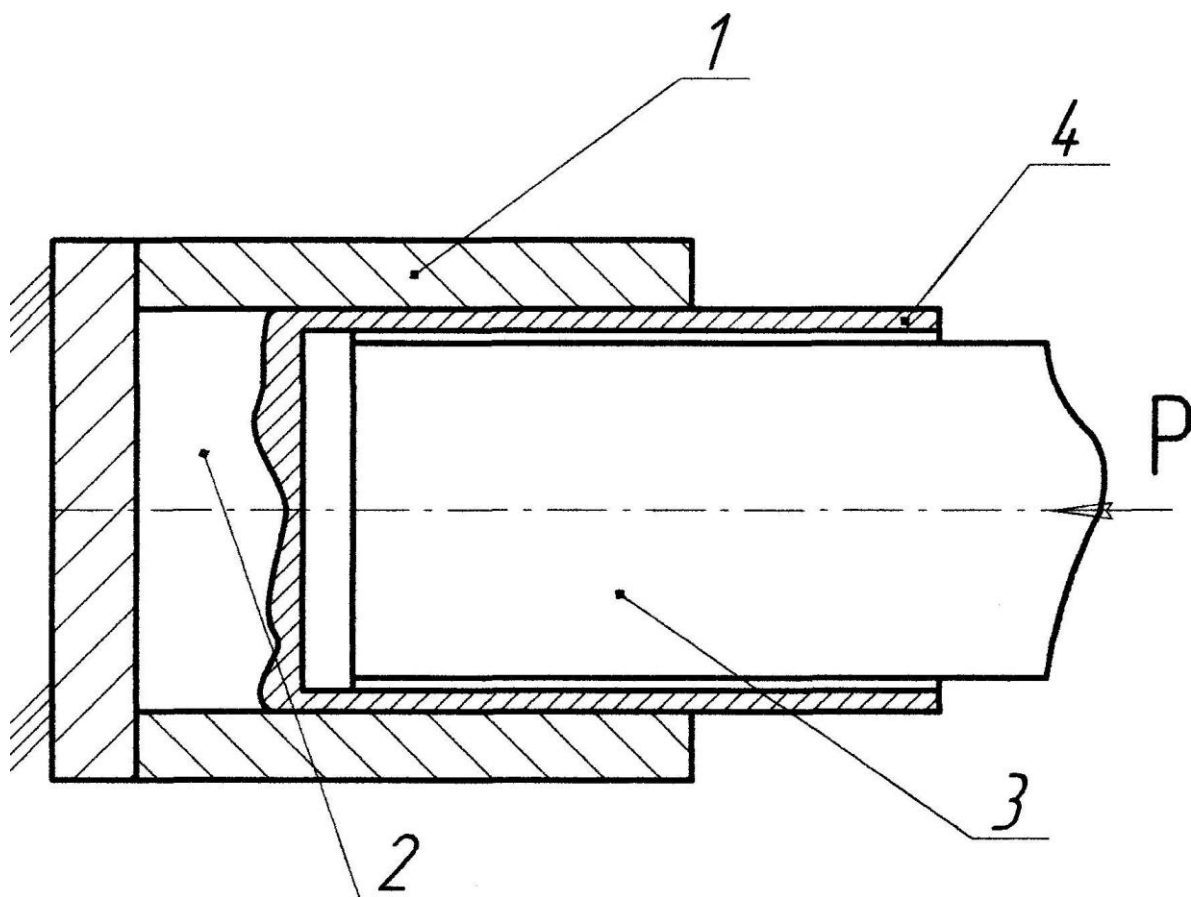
Схема зворотного пресування труб на пуансон
